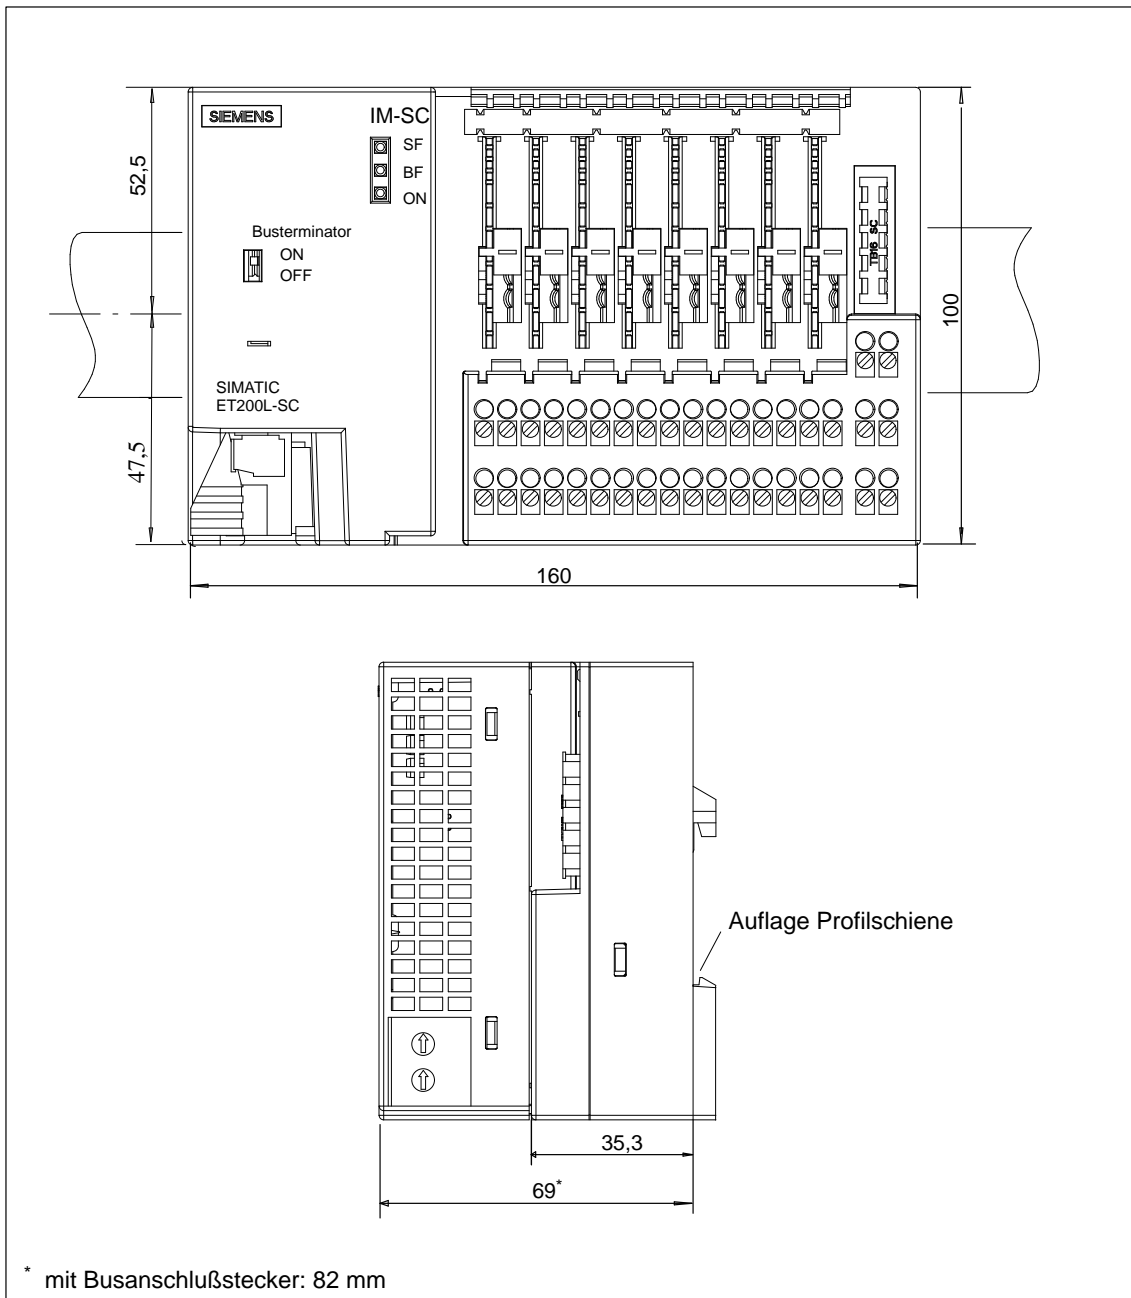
Terminalblock TB 16IM-SC mit aufgestecktem Interfacemodul IM-SC, Maßbild
